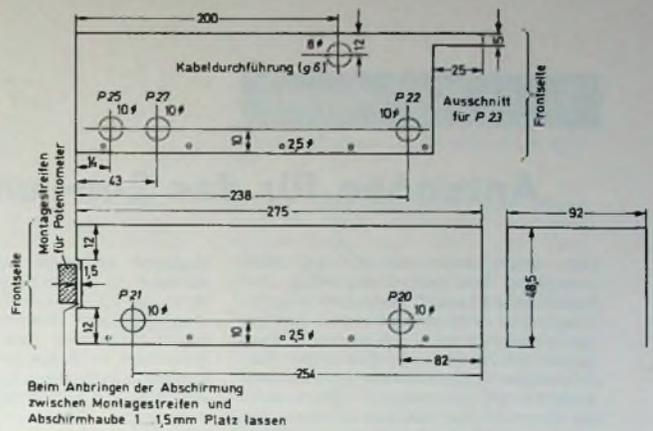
Abschirmhaube für die Baugruppe HS (die Bohrungen für die Befestigungsschrauben sind nur angedeutet; Material: Fe-Blech, 0,5 mm)
